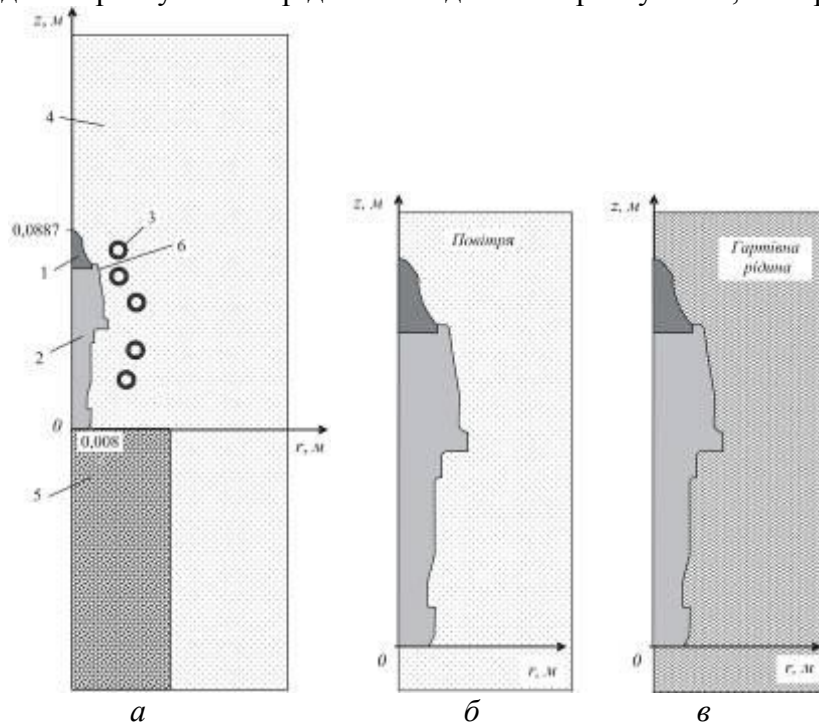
Розрахункові схеми (половина осьового перерізу просторової області) процесів: а – індукційного паяння різця; б – охолодження на повітрі; в – охолодження в гартівній рідині; 1 – твердосплавна вставка різця (сплав ВК8); 2 – сталева державка різця; 3 – витки індуктора (мідь); 4 – повітря; 5 – підставка (вогнетривка цегла); б – зона поверхні державки поблизу вставки
